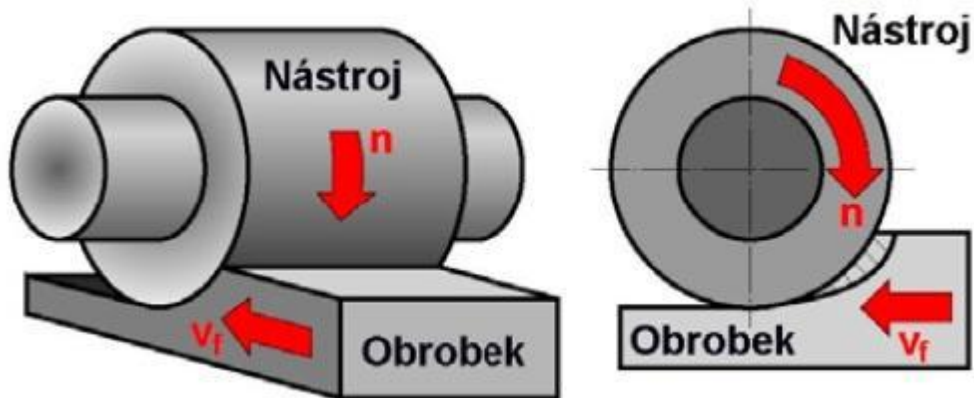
Frézování válcové (obvodové) a čelní[1]
